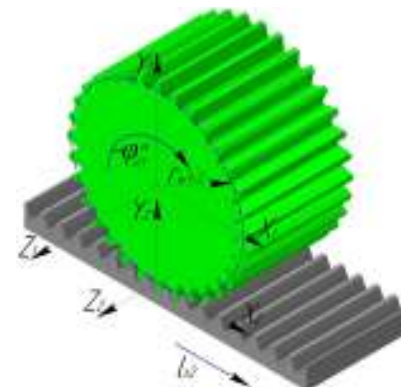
Кинематическая схема прямого формообразования, т.е. формообразования профилем впадины зубчатого колеса профилем зуба исходной формообразующей рейки
